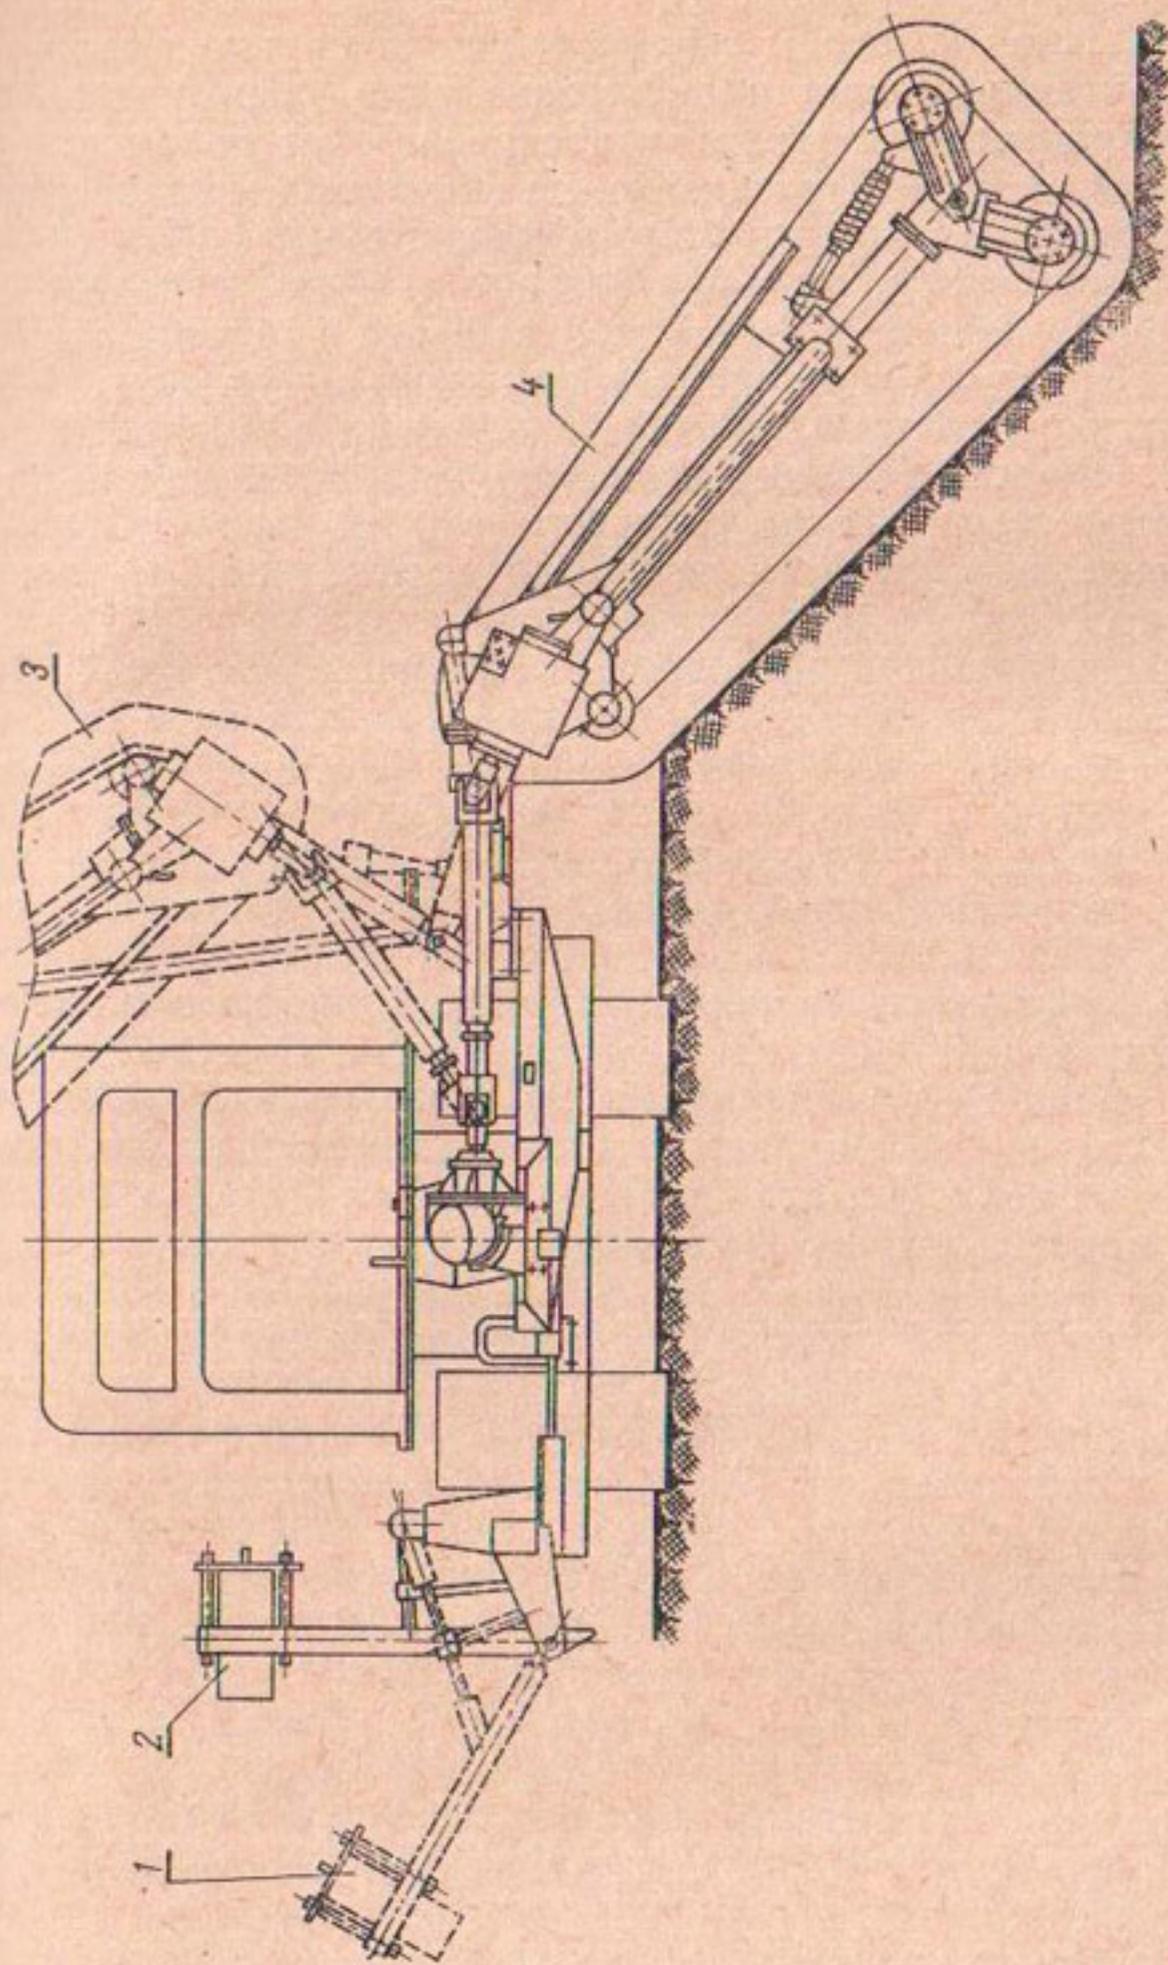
Конструкция навесного оборудования каналоочистителя Д-490М (скребковая цепь):
